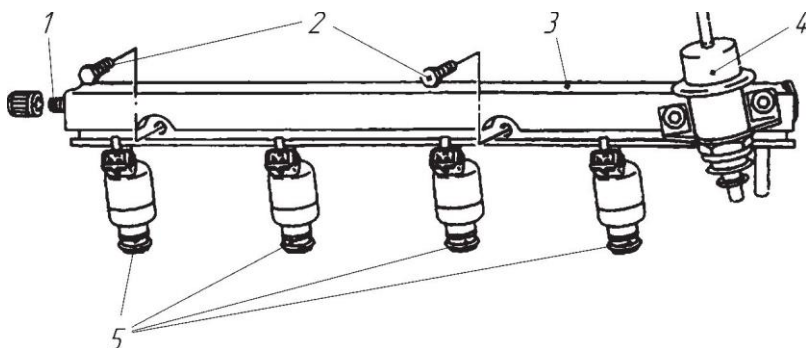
Топливная рампа в сборе: 1—штуцер для контроля давления топлива; 2 — болты крепления рампы; 3 — рампа; 4 — регулятор давления топлива; 5 — форсунки.
